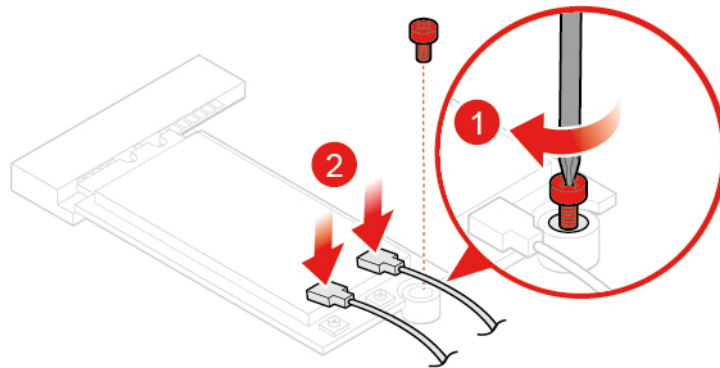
Collegamento dei cavi dell'antenna Wi-Fi
